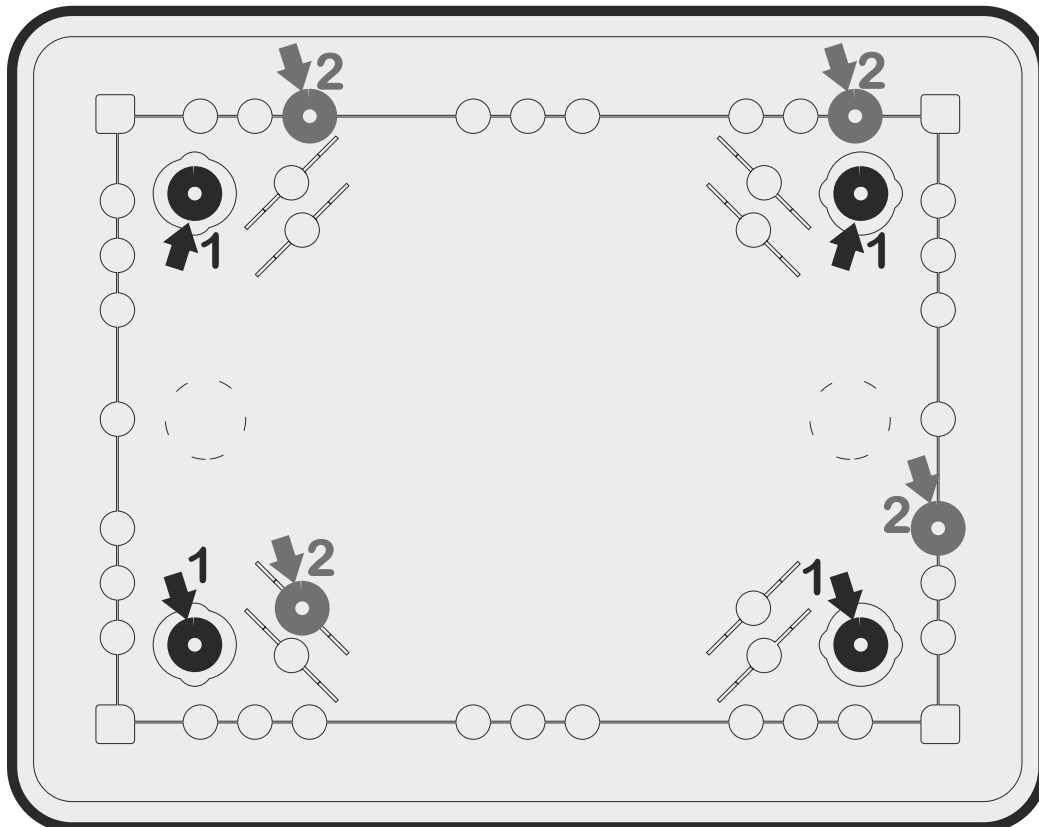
Ansicht des Gehäuses der Steuerung, die die Montageorte von Gehäuse [1] und Steuerung [2] zeigt.
